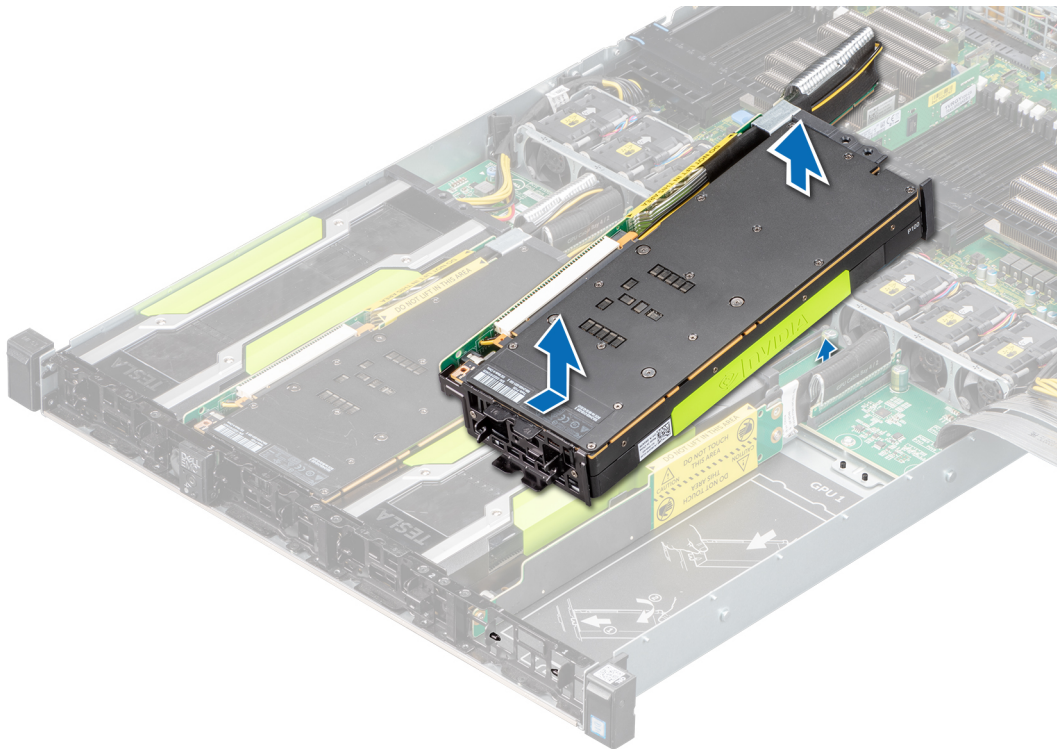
Entfernen einer GPU4 für die Konfigurationen B und G
